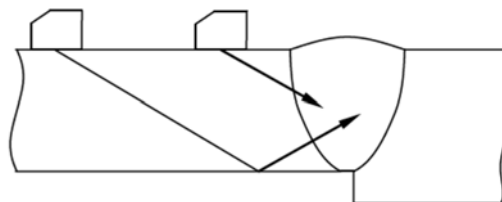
Схема контроля сварных соединений с разной толщиной свариваемых элементов
